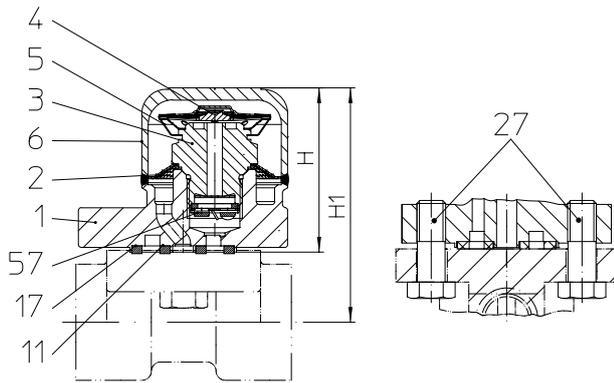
Universal-Flansch mit 2 x 3/8" UNC-Gewinde
